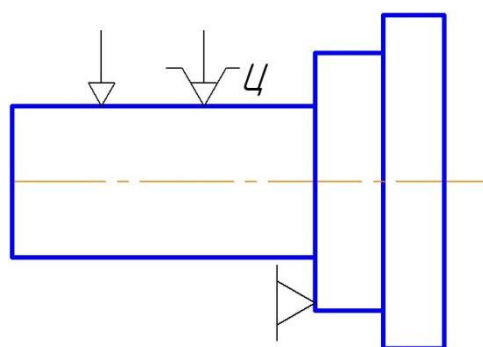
Умовна схема базування при шлифуванні внутрішніх поверхонь на внутрішньошлифувальних верстатах
